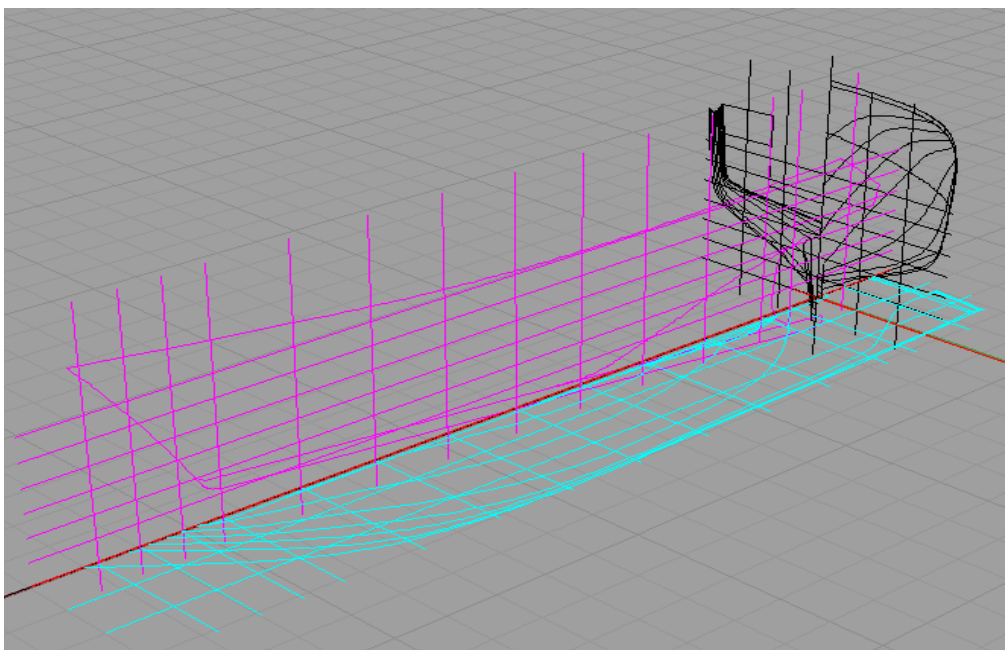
Vistas de alzado, planta y perfil, escaladas y giradas según los ejes más convenientes
